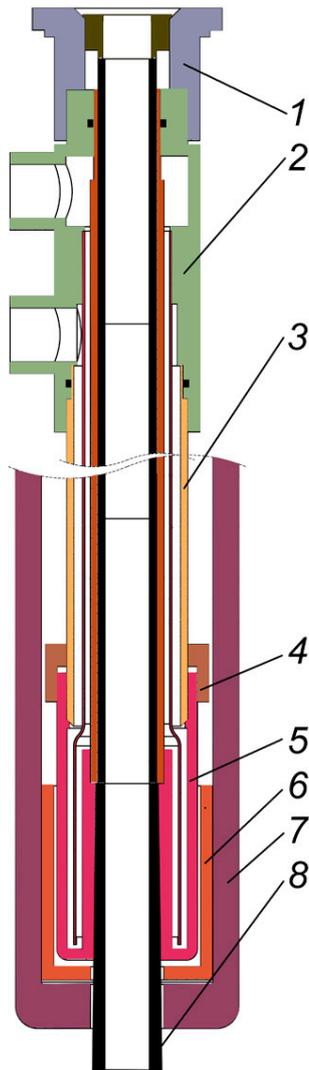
Установка непрерывного литья вверх на КУЗОЦМ
